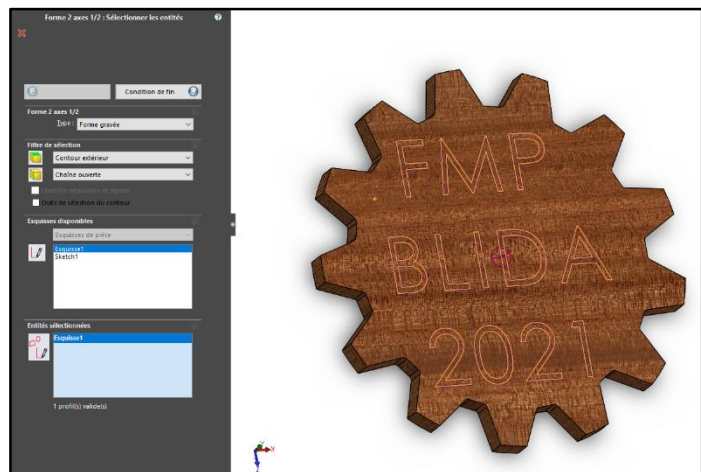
29 : Choix de la face d'usinage et les formes usinables
